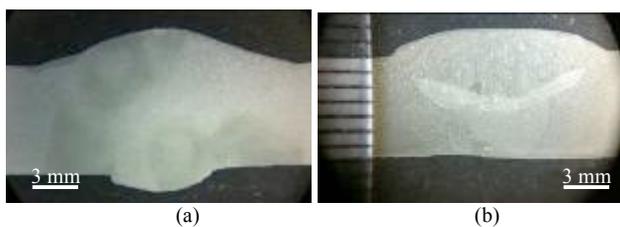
Ensaio macrográfico da amostra soldada com eletrodos revestidos SMAW (a) e com o processo combinado SMAW+FCAW-S (b)
